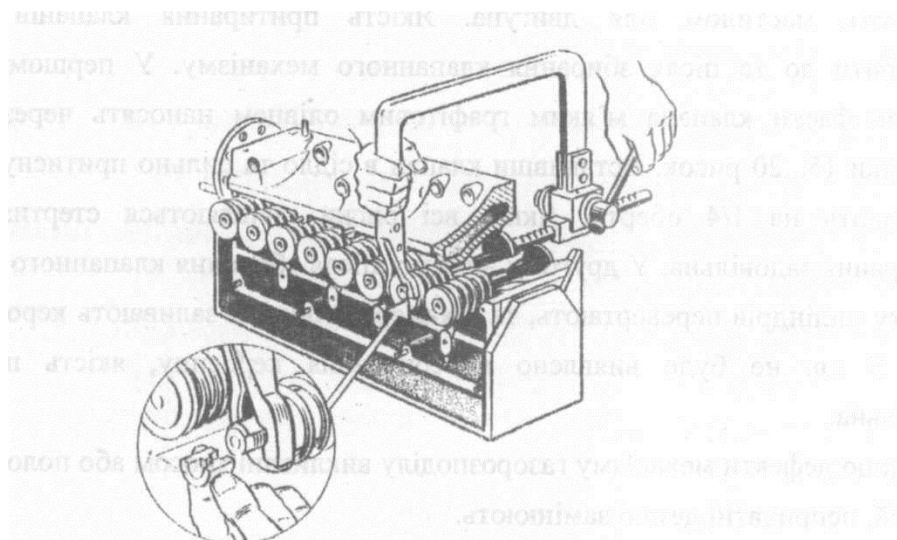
Зняття та встановлення клапанних пружин пристосуванням.
